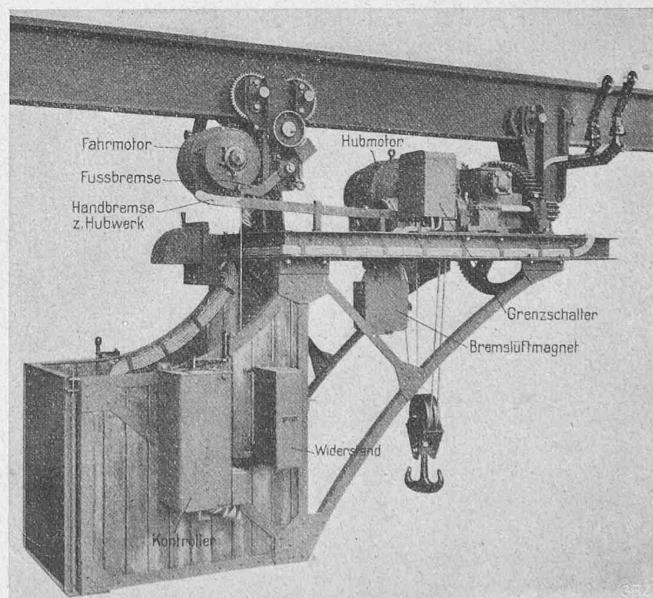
Motor-Laufwinde für 2 t — Maschinenfabrik Oerlikon
